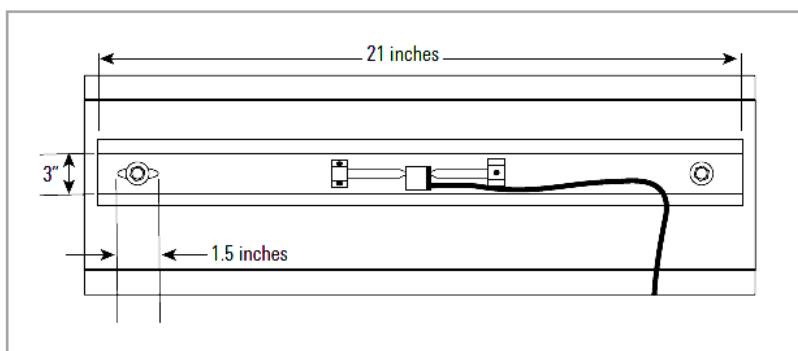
Установка закрывающей плиты. Вид сверху.
